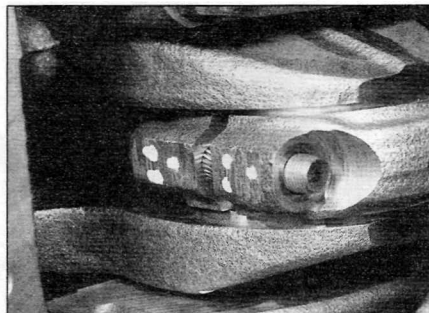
Идентификационная маркировка на шатуне и крышке подшипника нижней головки шатуна (показано для подшипника № 3)
